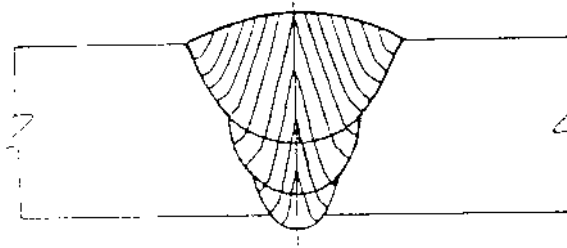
coupe transversale montrant le sens privilégié de croissance
